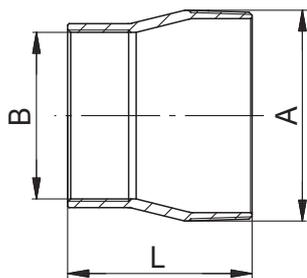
Габаритный чертеж и изображение переходника резьба-фланец
